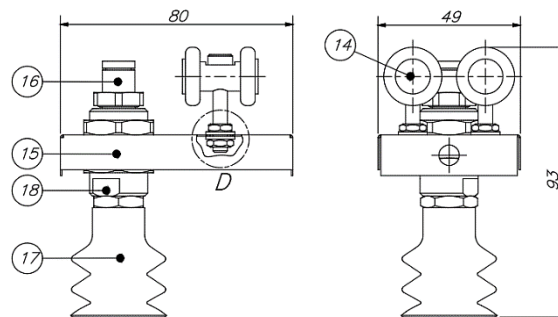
Ensamble de una ventosa - Plano PE1.4.3.2-A2
